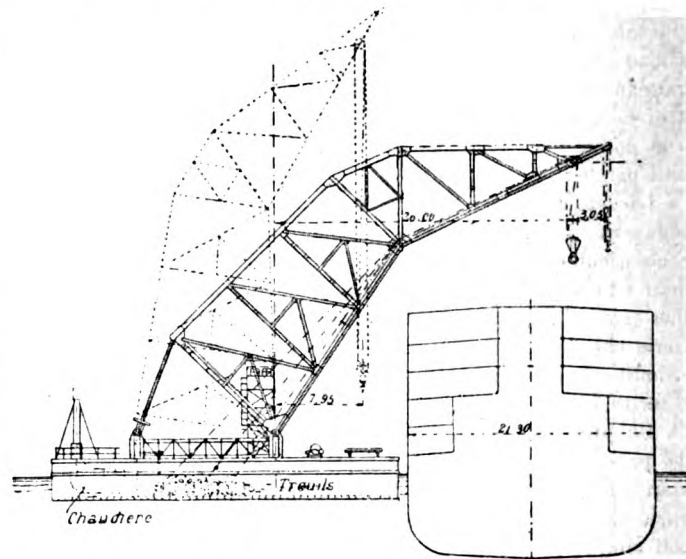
Gru galleggiante da 150 tonn. dei Cantieri di Kawasaki - Elevazione.
